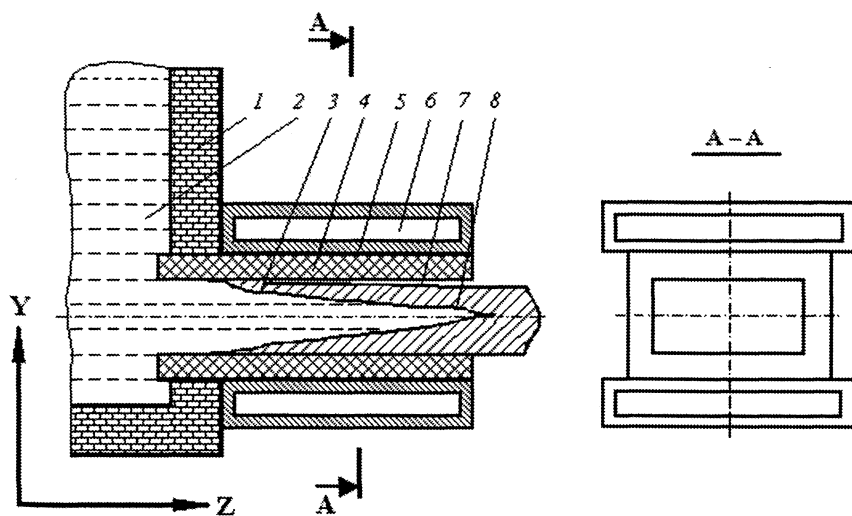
Схема процесса непрерывного горизонтального литья: 1 — металлоприемник; 2 — жидкий металл; 3 — начальная корка; 4 — графитовая вставка; 5 — стальной корпус; 6 — вода; 7 — зазор между отливкой и кристаллизатором; 8 — затвердевающая непрерывная отливка
